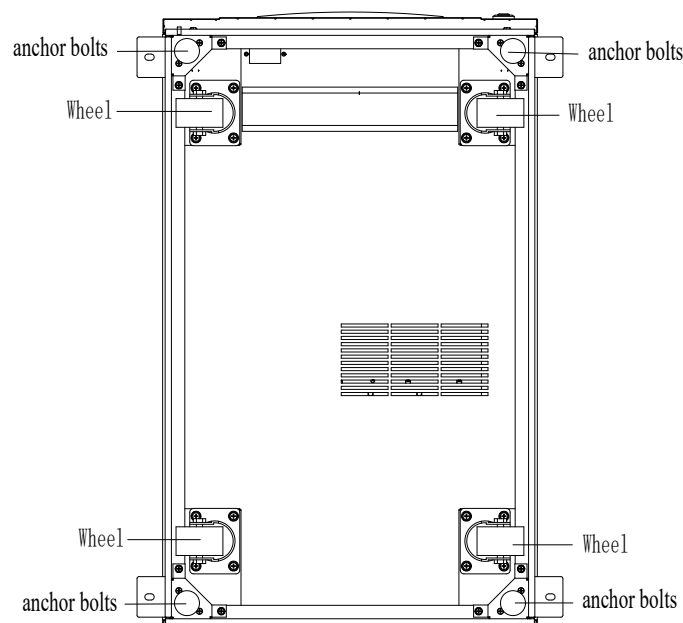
Vue de dessous de la structure porteuse de l'armoire
